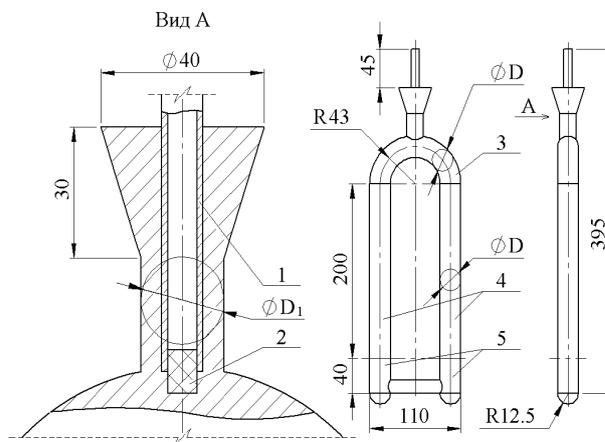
Схема разработанной конструкции блока отливок: 1 – трубка; 2 – пробка; 3 – коллектор; 4 – отливки; 5 – зумпф.
